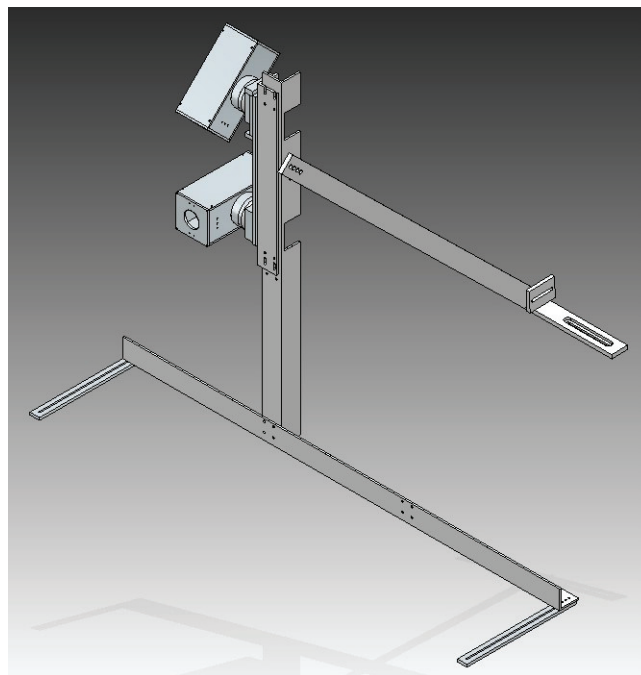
Rendu 3D de l'assemblage optomécanique pour la configuration de rotation planétaire du bâti de dépôt.
